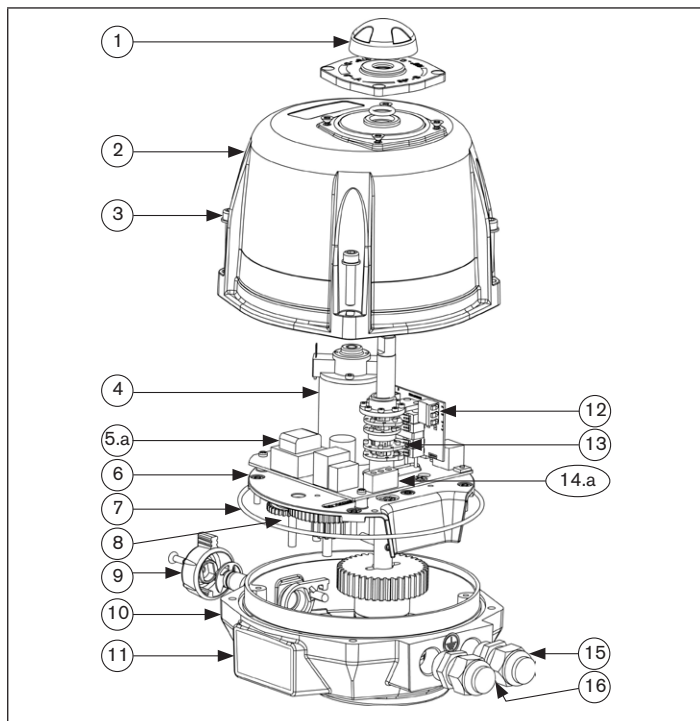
Explosionsdarstellung Motor 25 - 75 Nm
